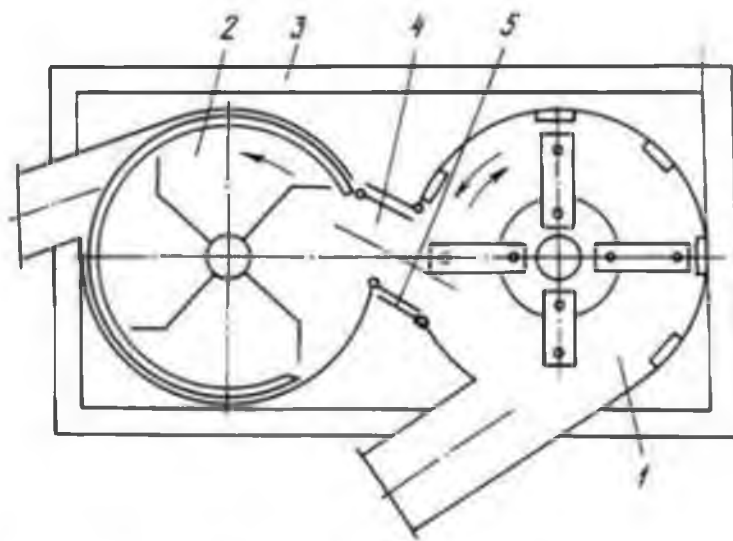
Дробарка з двома робочими органами: 1 – молоткова дробарка; 2 – ріжуча машина; 3 – рама; 4 – з'єднувальний канал; 5 – стінки каналу
